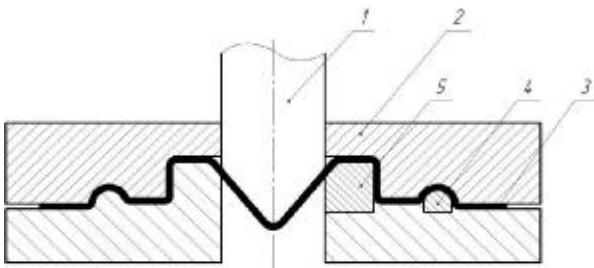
Схема оценки эффективности торможения фланца заготовки: 1 – пуансон; 2 – прижимная плита; 3 – заготовка; 4 – перетяжное ребро; 5 – перетяжной порог
